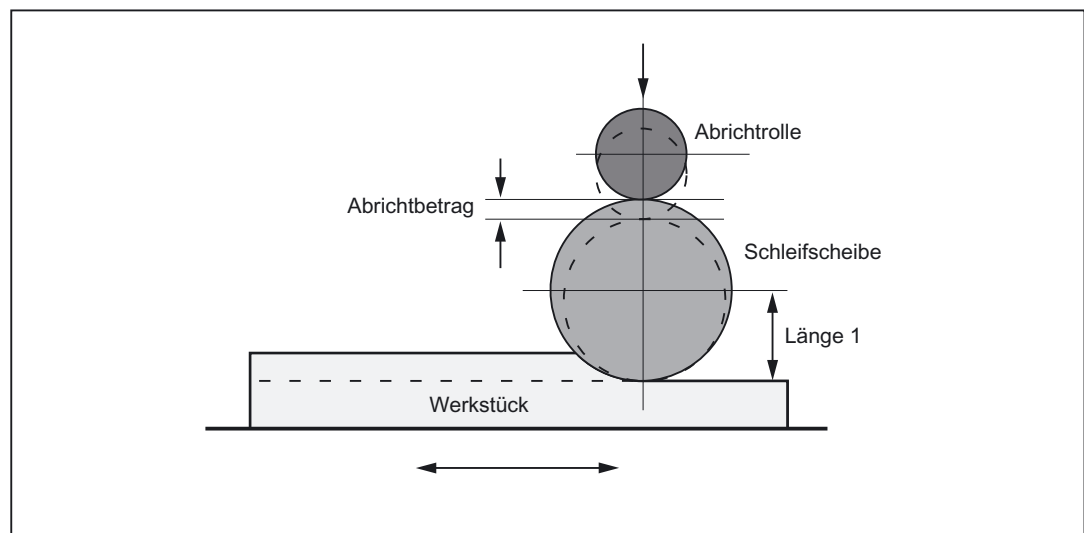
Abrichten während der Bearbeitung mit einer Abrichtrolle
